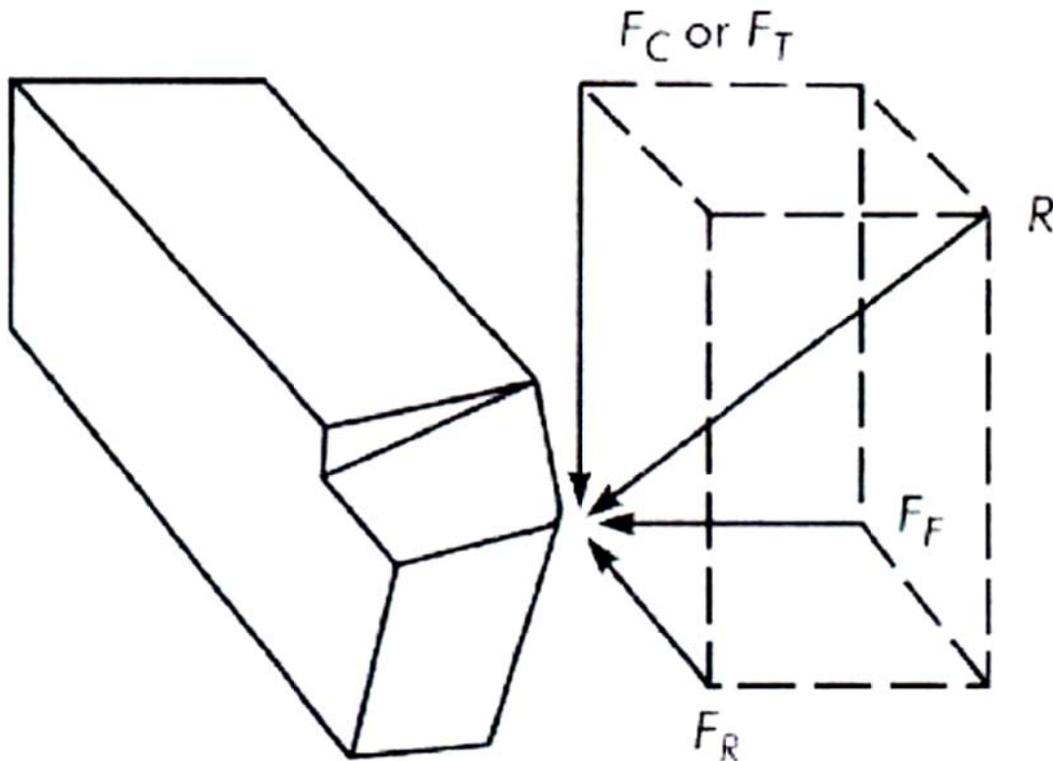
Componentes de la fuerza de corte actuando sobre la herramienta de corte
